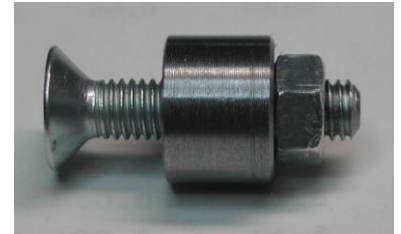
Vorrichtung zum sauberen Bearbeiten von gekürzten Schrauben
